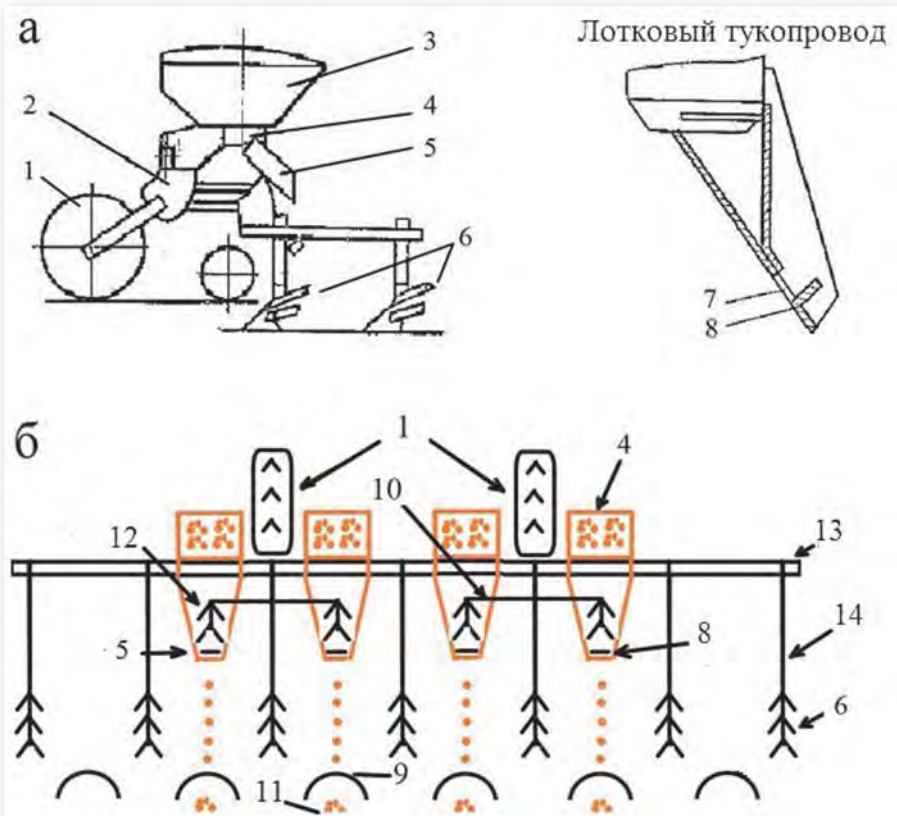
Схема переоборудования культиватора для предпосадочной нарезки гребней с одновременным внесением минеральных удобрений: а – вид сбоку, б – вид сверху. 1 – опорное колесо; 2 – кронштейн; 3 – бункер; 4 – туковысевающий аппарат; 5 – лоток; 6 – трехъярусные окучники; 7 – окно; 8 – экран; 9 – вершина нарезаемого гребня; 10 – квадратный брус; 11 – удобрения; 12 – двухъярусная лапа; 13 – брус культиватора; 14 – грядиль. Примечание: двухъярусная лапа шириной 220 мм, трехъярусный окучник – 330 мм.
